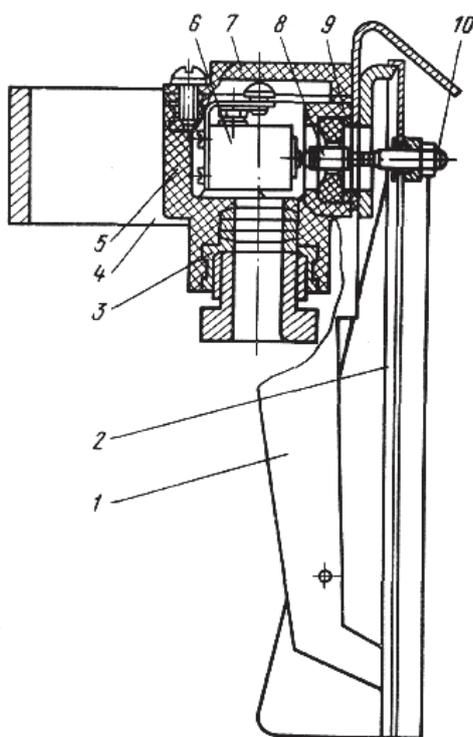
Маятниковый измерительный преобразователь уровня сыпучих материалов СУ-1Ф: 1 – упор; 2 – флажок; 3 – сальниковое уплотнение кабельного ввода; 4 – кронштейн; 5 – корпус; 6 – микропереключатель типа МП-2101; 7 – крышка; 8 – шток; 9 – резиновая прокладка; 10 – регулировочный винт
